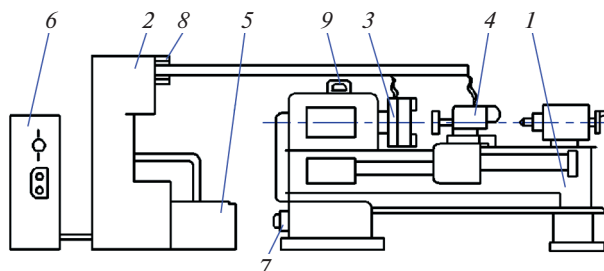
Оборудование для комбинированной обработки на базе универсального токарного станка: 1 – универсальный токарно-винторезный станок; 2 – источник тока; 3 – планшайба патрона; 4 – приспособление; 5 – гидростанция для охлаждения источника тока; 6 – электрошкаф; 7 – мотор-редуктор для уменьшения скорости вращения шпинделя; 8 – трансформатор; 9 – амперметр для контроля величины силы тока.
